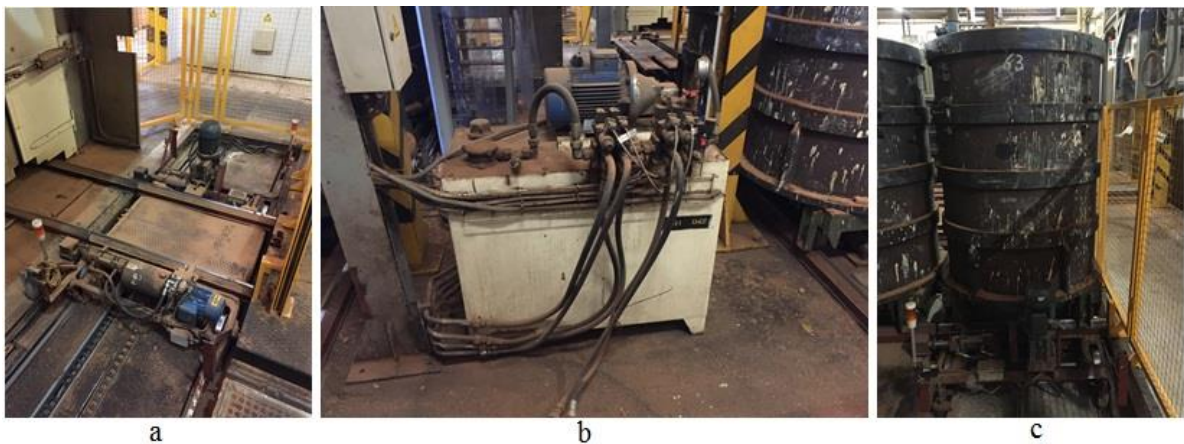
a)Transfer b)Central hidráulica c)Movimentação de um molde
